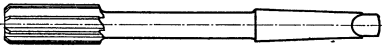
Maschinenreibahle mit kegelförmigem Schaft.
